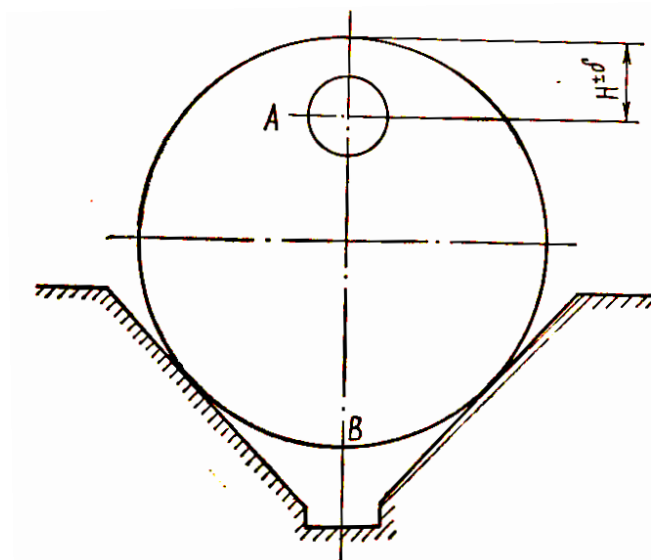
Схема установки детали в призму для сверления отверстия с выдерживанием размера $H \pm \delta$
